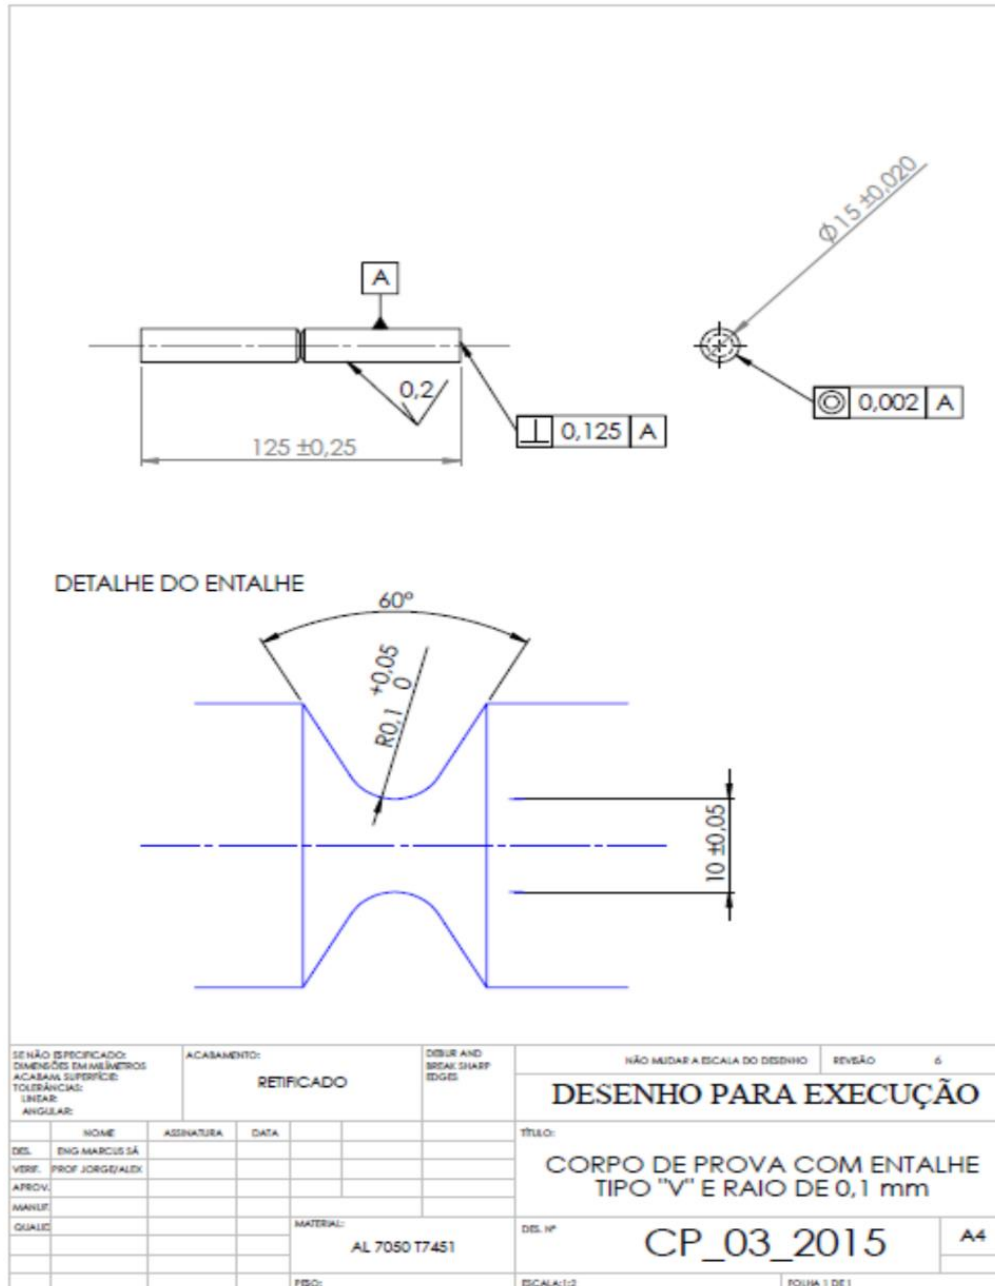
Desenho técnico do corpo de prova com entalhe.
